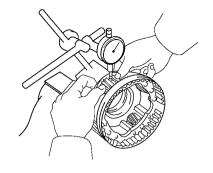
用塞尺测量行星小齿轮的轴向间隙
